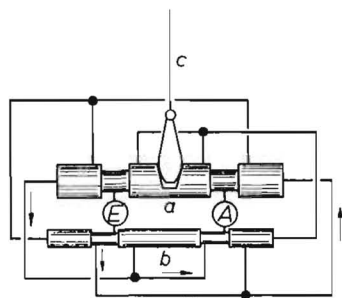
Schema der Umsteuerung mit einem Steuerkolben
